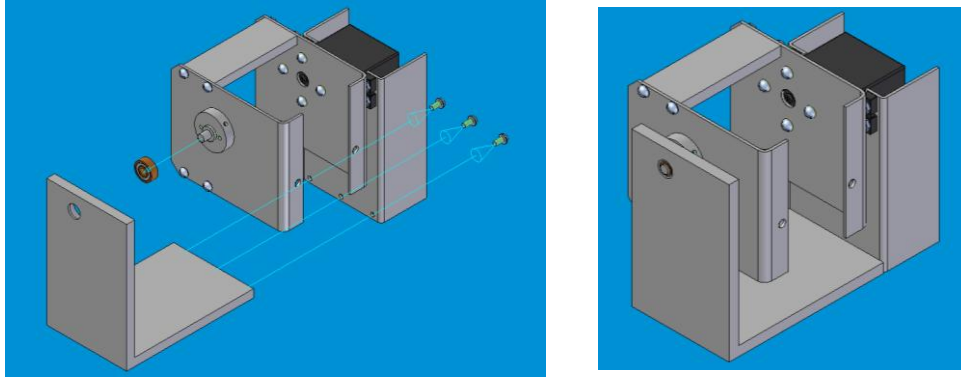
Unión de las dos piezas de la base del sistema. El rodamiento se coloca entre el eje y la pieza izquierda de la base.
